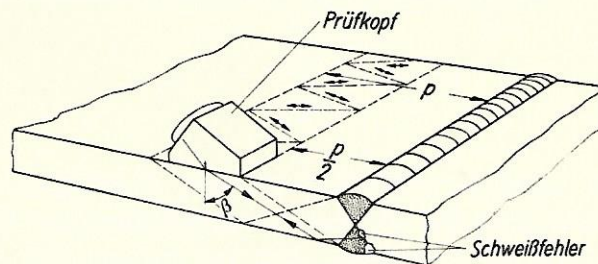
Schweißnahtprüfung mit einem Winkelkopf
